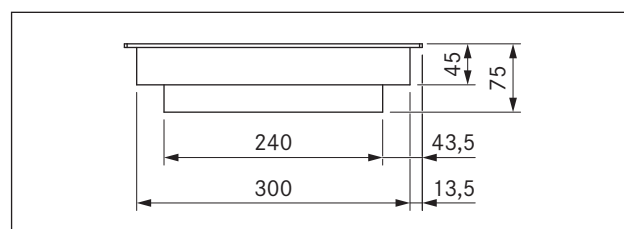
Dimensões do aparelho CKCH, vista frontal
